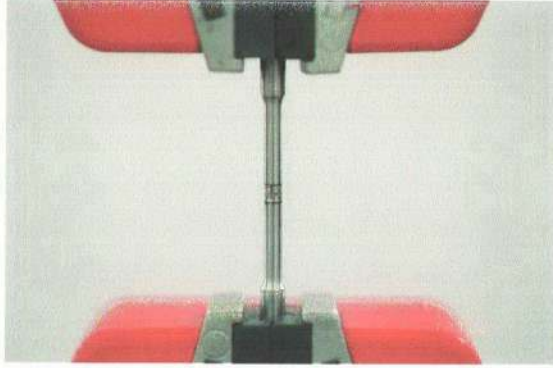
Lazer kaynakla birleştirilmiş örnekler. Kaynak alanı; 3.3 mm
